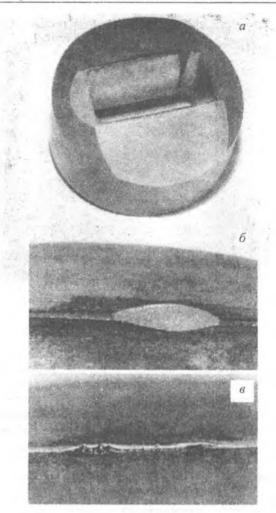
Внешний вид обсечного пуансона (a); характер усталостного разрушения режущей кромки (б) и износа рабочей поверхности (a)
